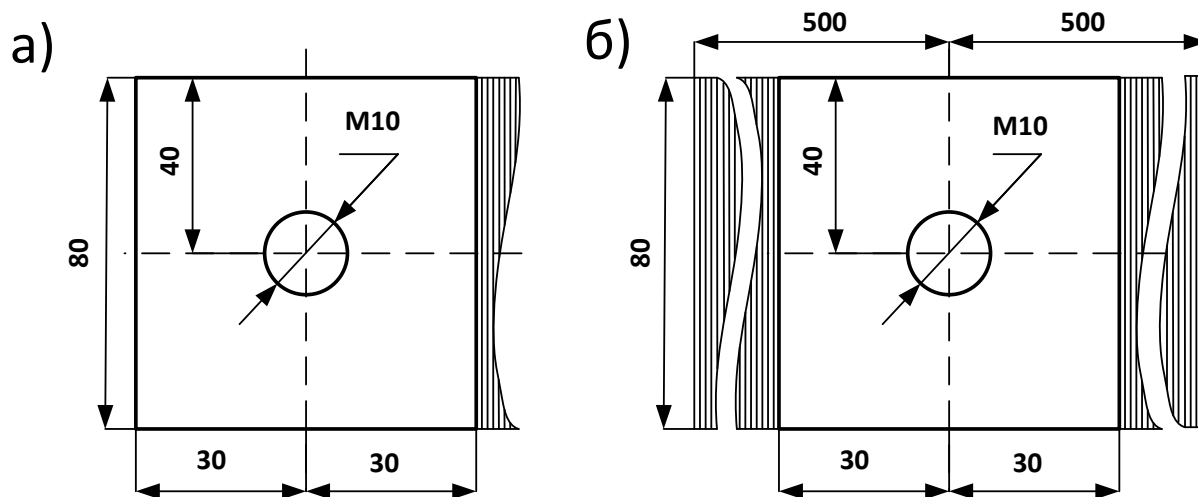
Размеры монтажных площадок для шин сечением 80x4мм² (а-размещение по краям; б-дополнительные)
